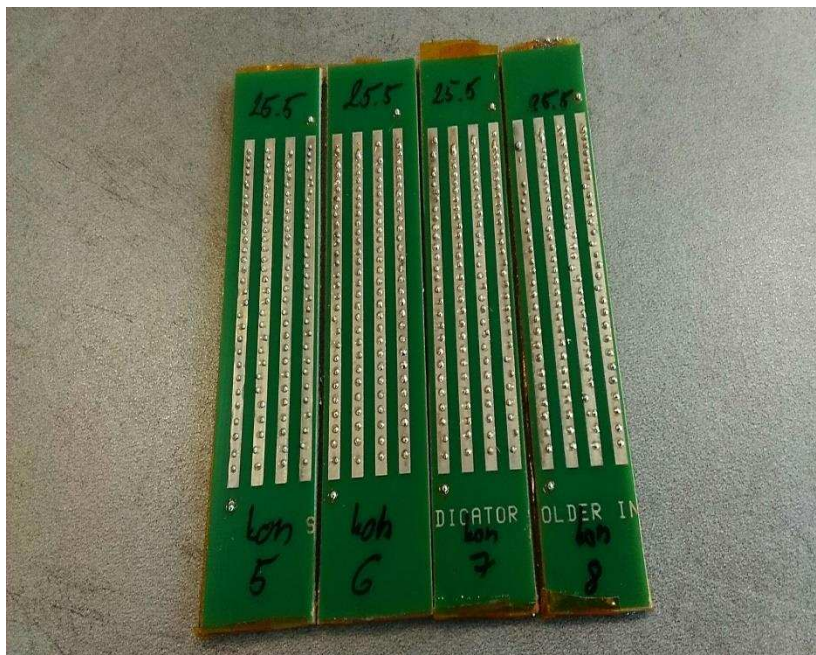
Solder indicator – imerzní cín po 1. přetavení
